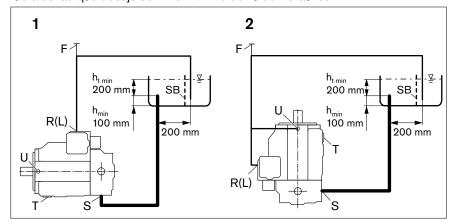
Montaje bajo el tanque con posición de montaje horizontal 1 y vertical 2
